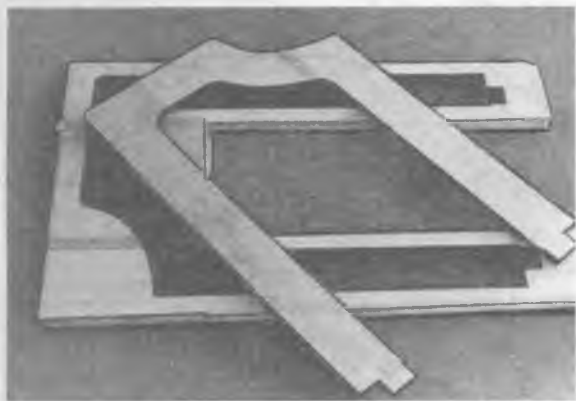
Деталь боковины кресла, изготовленная с применением лазера
